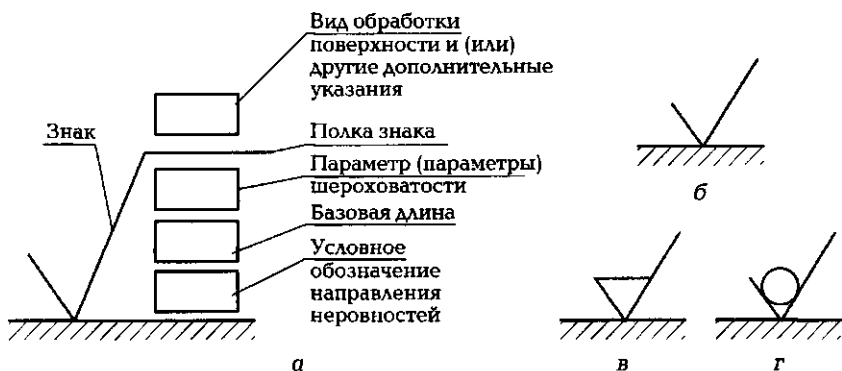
Структура обозначения шероховатости поверхности на чертежах:
